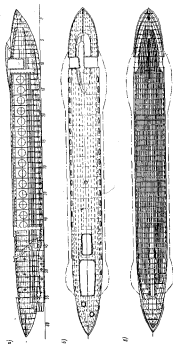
Конструктивные схемы корпуса и надстройки теплохода «Чайка»: а — продольный разрез; б — план верхней палубы; в — план днища.
